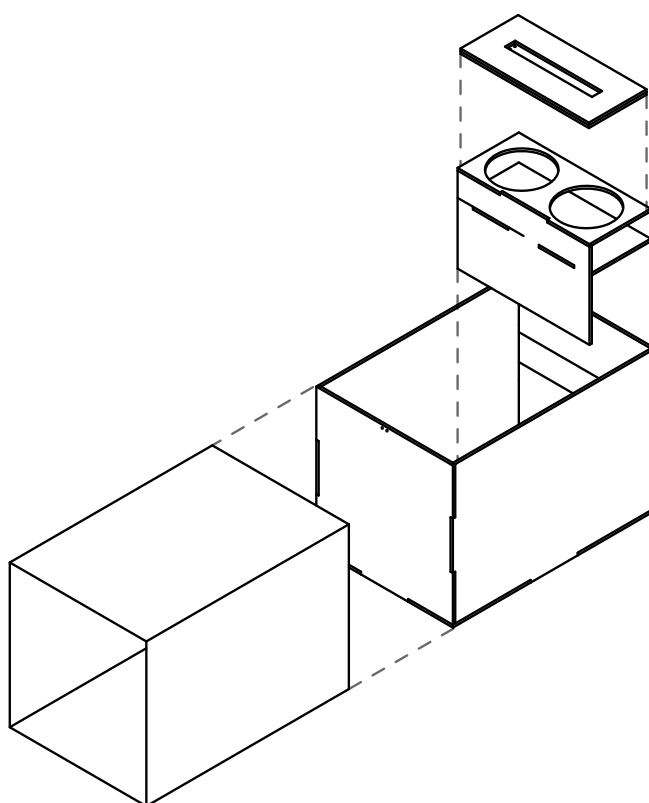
Detalhamento da embalagem: parte externa Fonte: Acervo da autora.
